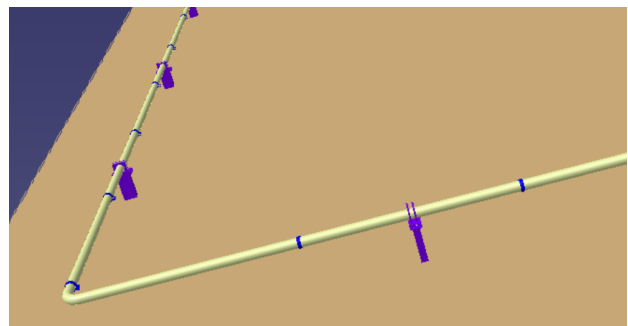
Installation 2 - Avec les fixations sur le sol
